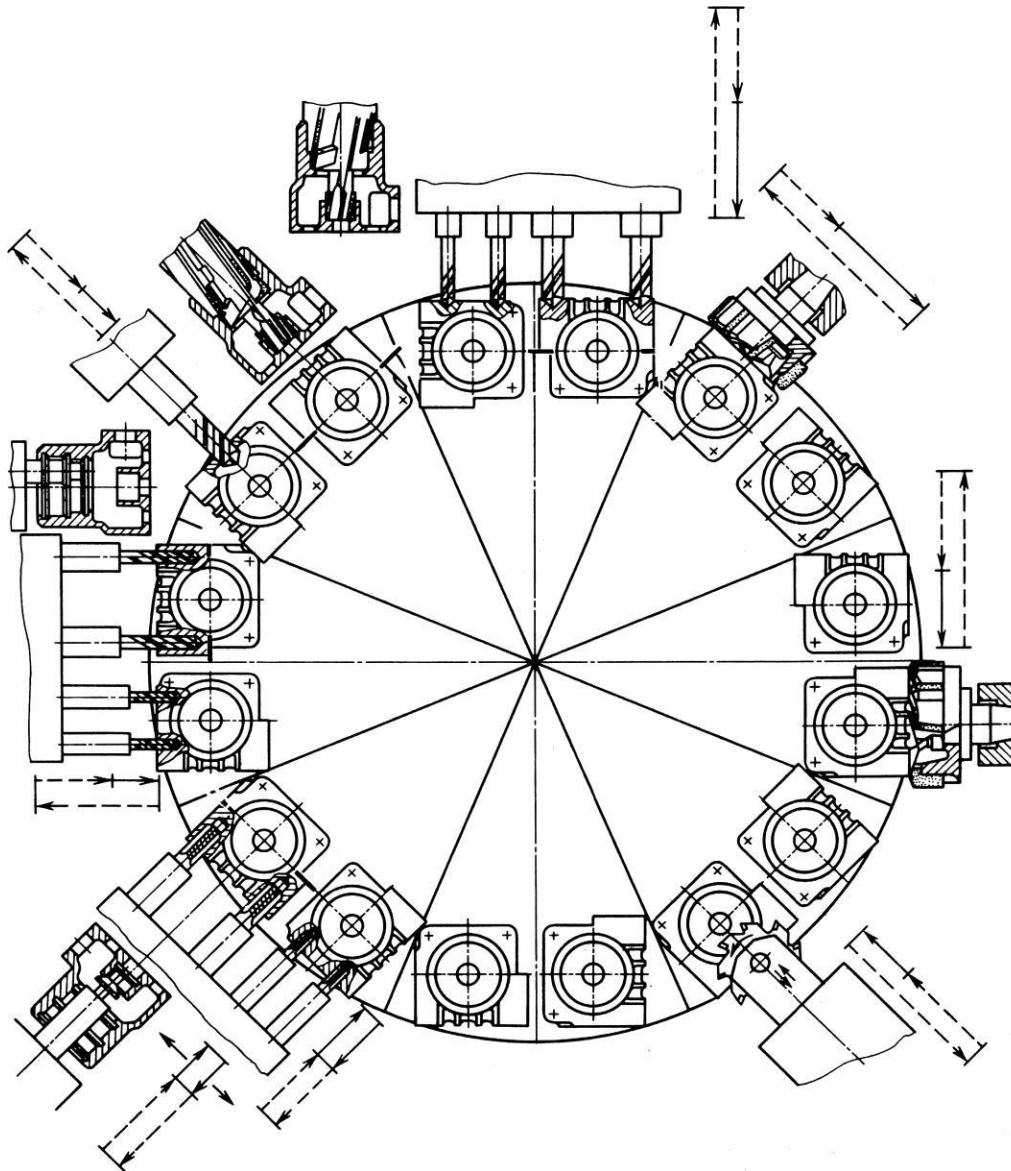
Схема обробки корпусу на агрегатному верстаті
